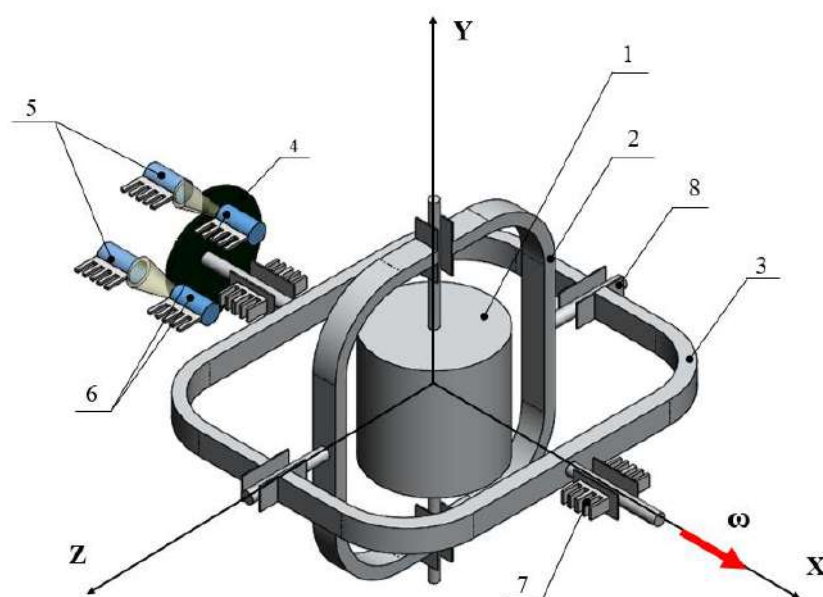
Типовая конструкция трехстепенного механического гироскопа для ИИСО БПЛА малого времени полета: 1 – ротор; 2 – внутренняя рамка; 3 – наружная рамка; 4 – модулирующий диск; 5 – фотодиоды; 6 – диоды; 7 – корпус (показан условно); 8 – опоры вращения (шарикоподшипники)
